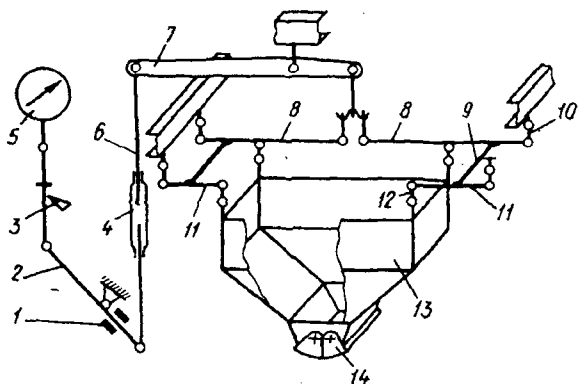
Весовой механизм дозатора минеральных материалов: 1 – тарная гиря; 2 – тарная рейка; 3 – ограничитель хода; 4 – регулировочный механизм; 5 – весовая головка; 6 – тяга; 7 – коромысло; 8, 11 – грузоподъемные рычаги; 9 – поперечина; 10 – подвеска рычагов; 12 – подвесные серьги; 13 – весовой бункер; 14 – затвор весового бункера.
